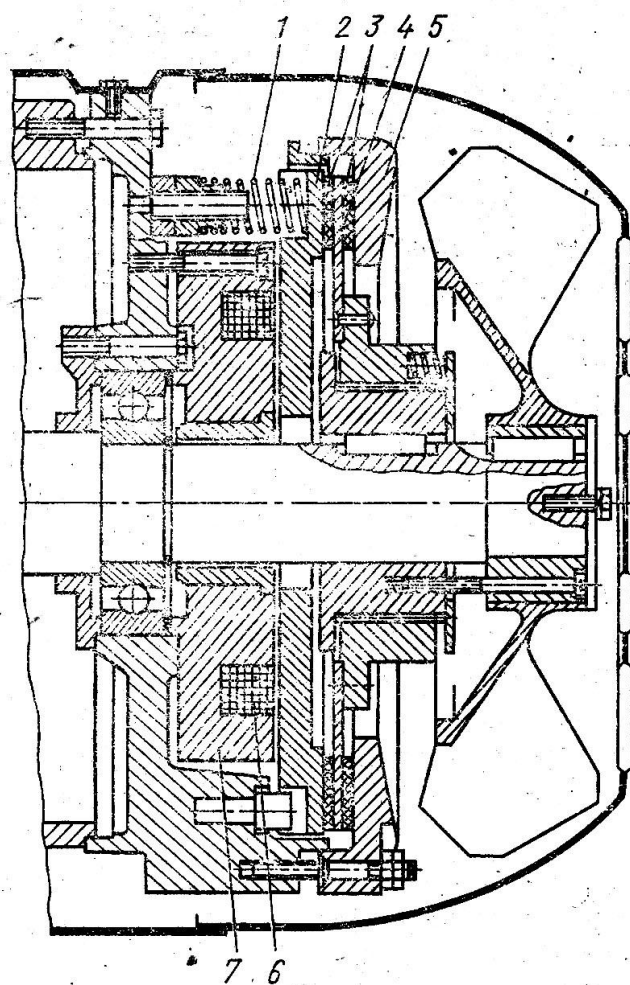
Тормозное устройство двигателя 4A160E.
